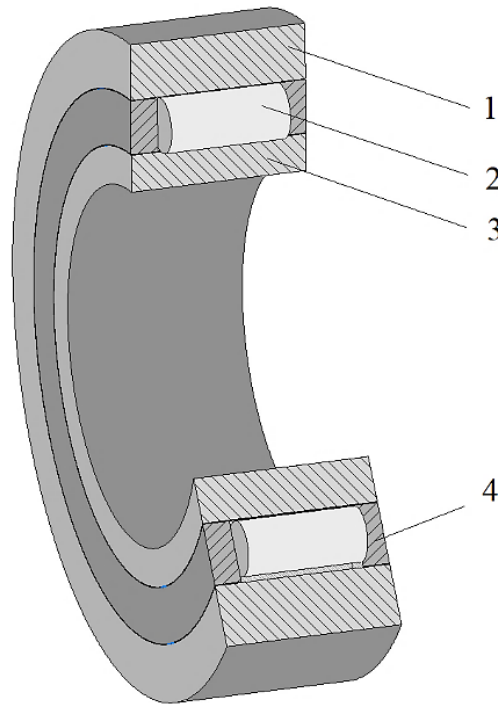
Роликовый цилиндрический подшипник:
